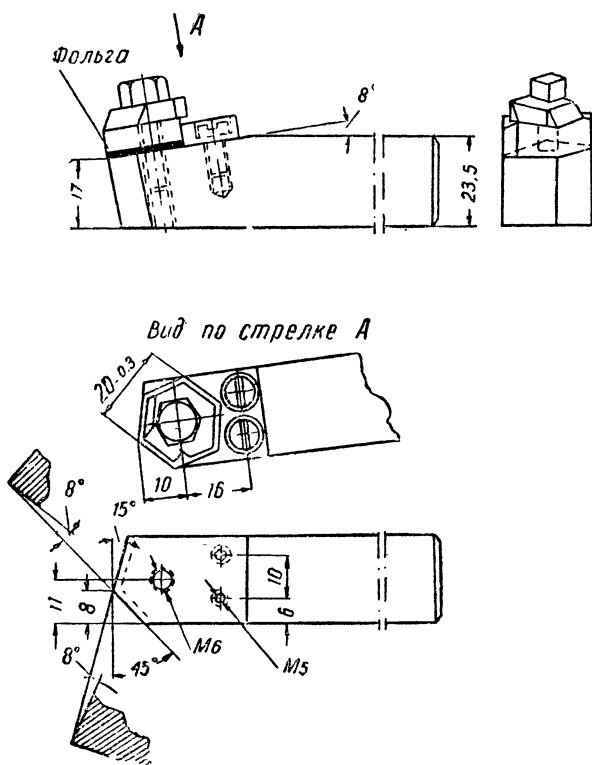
Державка для проходного резца с пластинкой шестигранной формы для обработки чугуна.
